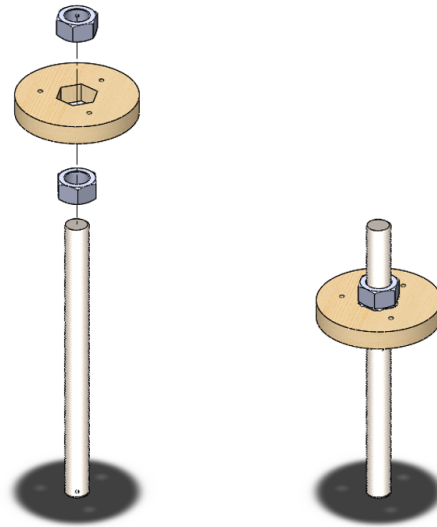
Vue éclatée et assemblage réalisé entre la tige filetée et le disque en bois
